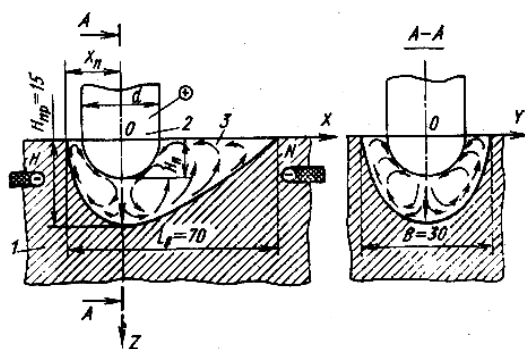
Модель сварочной ванны и схема движения металла в ней
